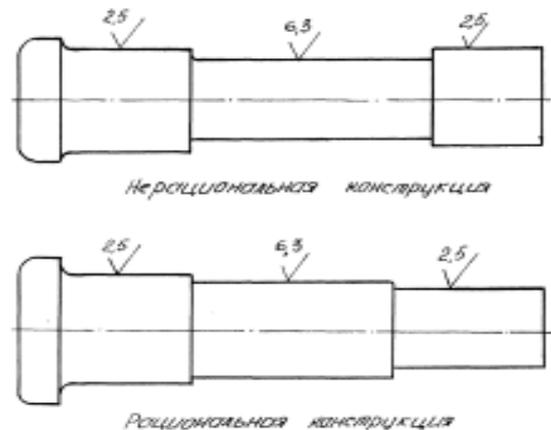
Различные расположения ступеней наружной цилиндрической поверхности
